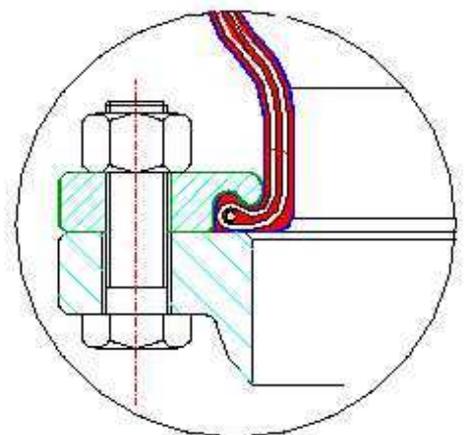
Adesione della parte in gomma del giunto con la flangia metallica della tubolatura/macchinario. Si noti il particolare montaggio del bullone.
